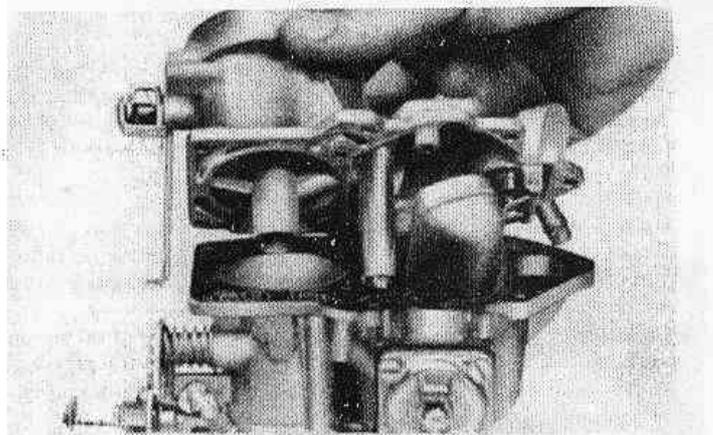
Снятие верхней половины корпуса карбюратора (Разд. 22)
